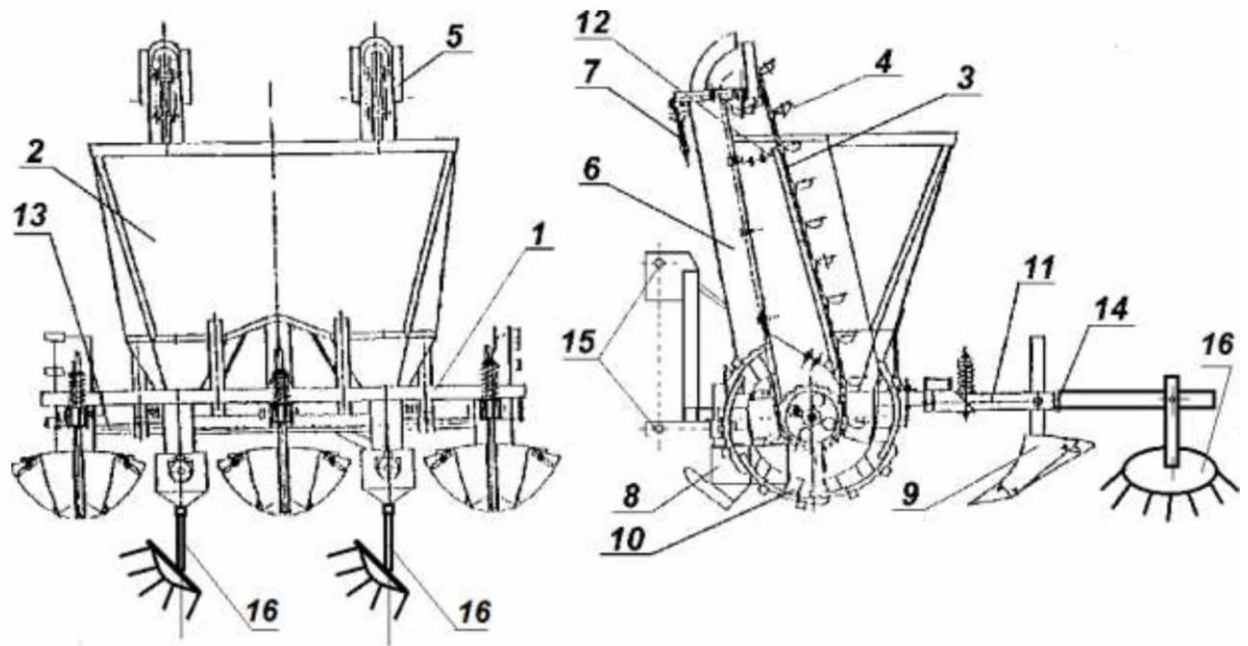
Схема дообладнання тракторної картоплесаджалки дисковими голчастими боронами: 1 - рама, 2 - бункер, 3 - ланцюговий транспортер, 4 - черпаки, 5 - садильний агрегат, 6 - зсипна труба, 7 - натяжний пристрій ланцюга, 8 - дисковий сошник, 9 - загортальна полиця, 10 - опорне колесо; 11 - важіль полиці для загортання, 12 - струшуваний агрегат; 13 - осьовий агрегат, 14 - тримачі, 15 - підвіска. [28]
